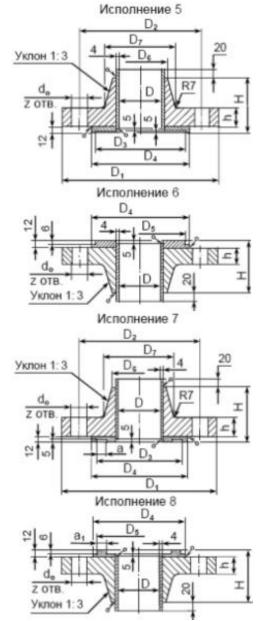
Фланцы стальные приварные встык, облицованные листом из коррозионностойкой стали. Исполнения фланцев: 5 — с впадиной; 6 — с выступом; 7 — с пазом; 8 — с шипом. Обозначенные размеры приведены в [3].
